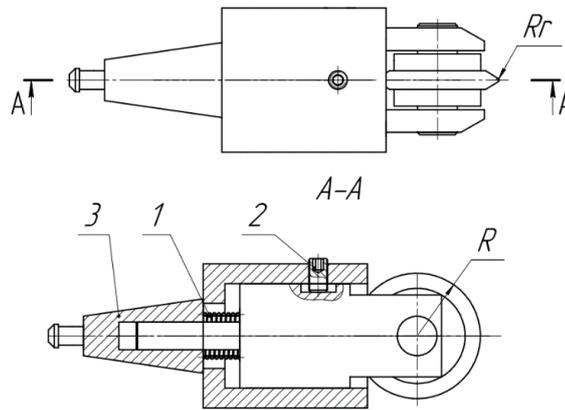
Эскиз приспособления для обкатывания ($R=54$ мм, $r=0,8$ мм). 1 – упругий элемент, 2 – установочный винт, тороидальный ролик, 3 – инструментальный конус
